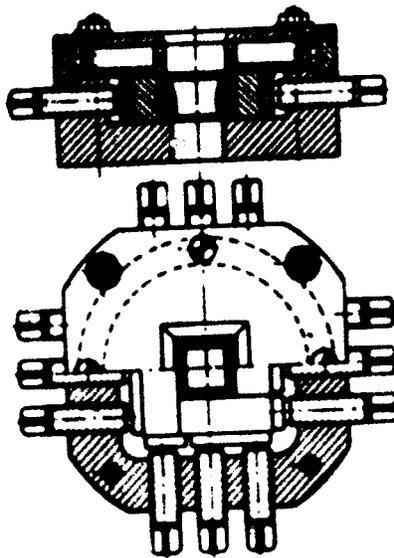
Verteilbares rechteckiges Ziehwerkzeug
